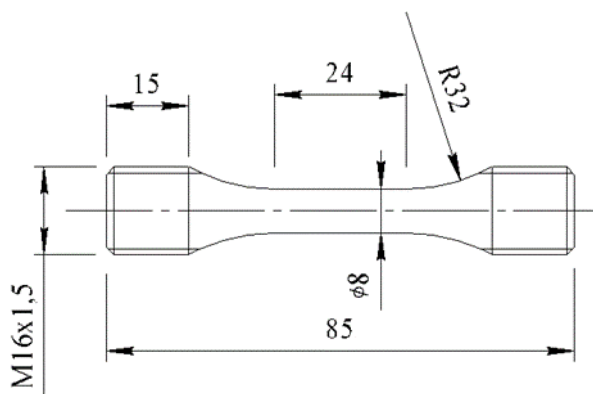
Образец для испытаний по ASTM E606
